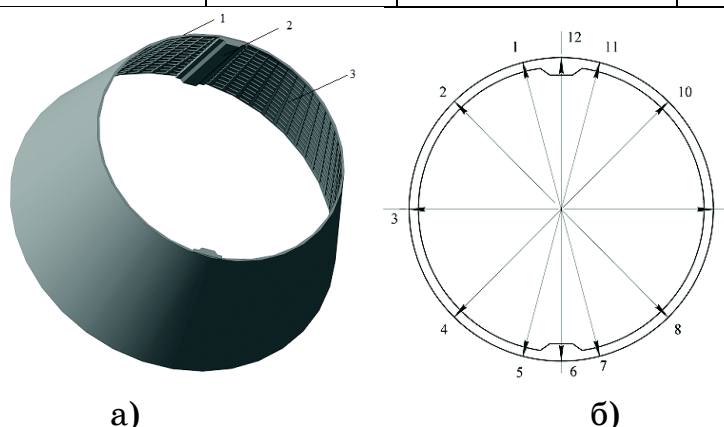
Общий вид конической обечайки с основными конструктивными элементами (1 – торцевой шпангоут, 2 – балка функционального стыка, 3 – вафельный фон)
